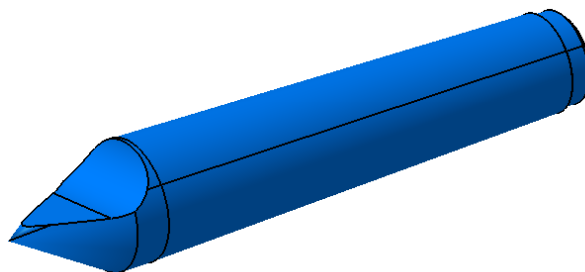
Přídavné zařízení připravené pro obrábění mezi hroty
